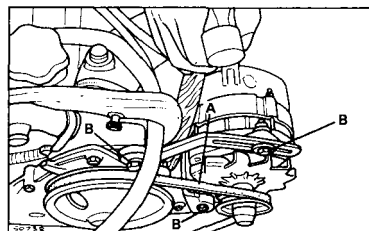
Проверка натяжения клиновидного ремня (A) и регулировка его после ослабления болтов (B)
